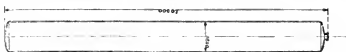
Geschweißter Gaskessel. Inhalt 50 cm, Prüfungsdruck 20 kg/cm, Gewicht 12100 kg.
